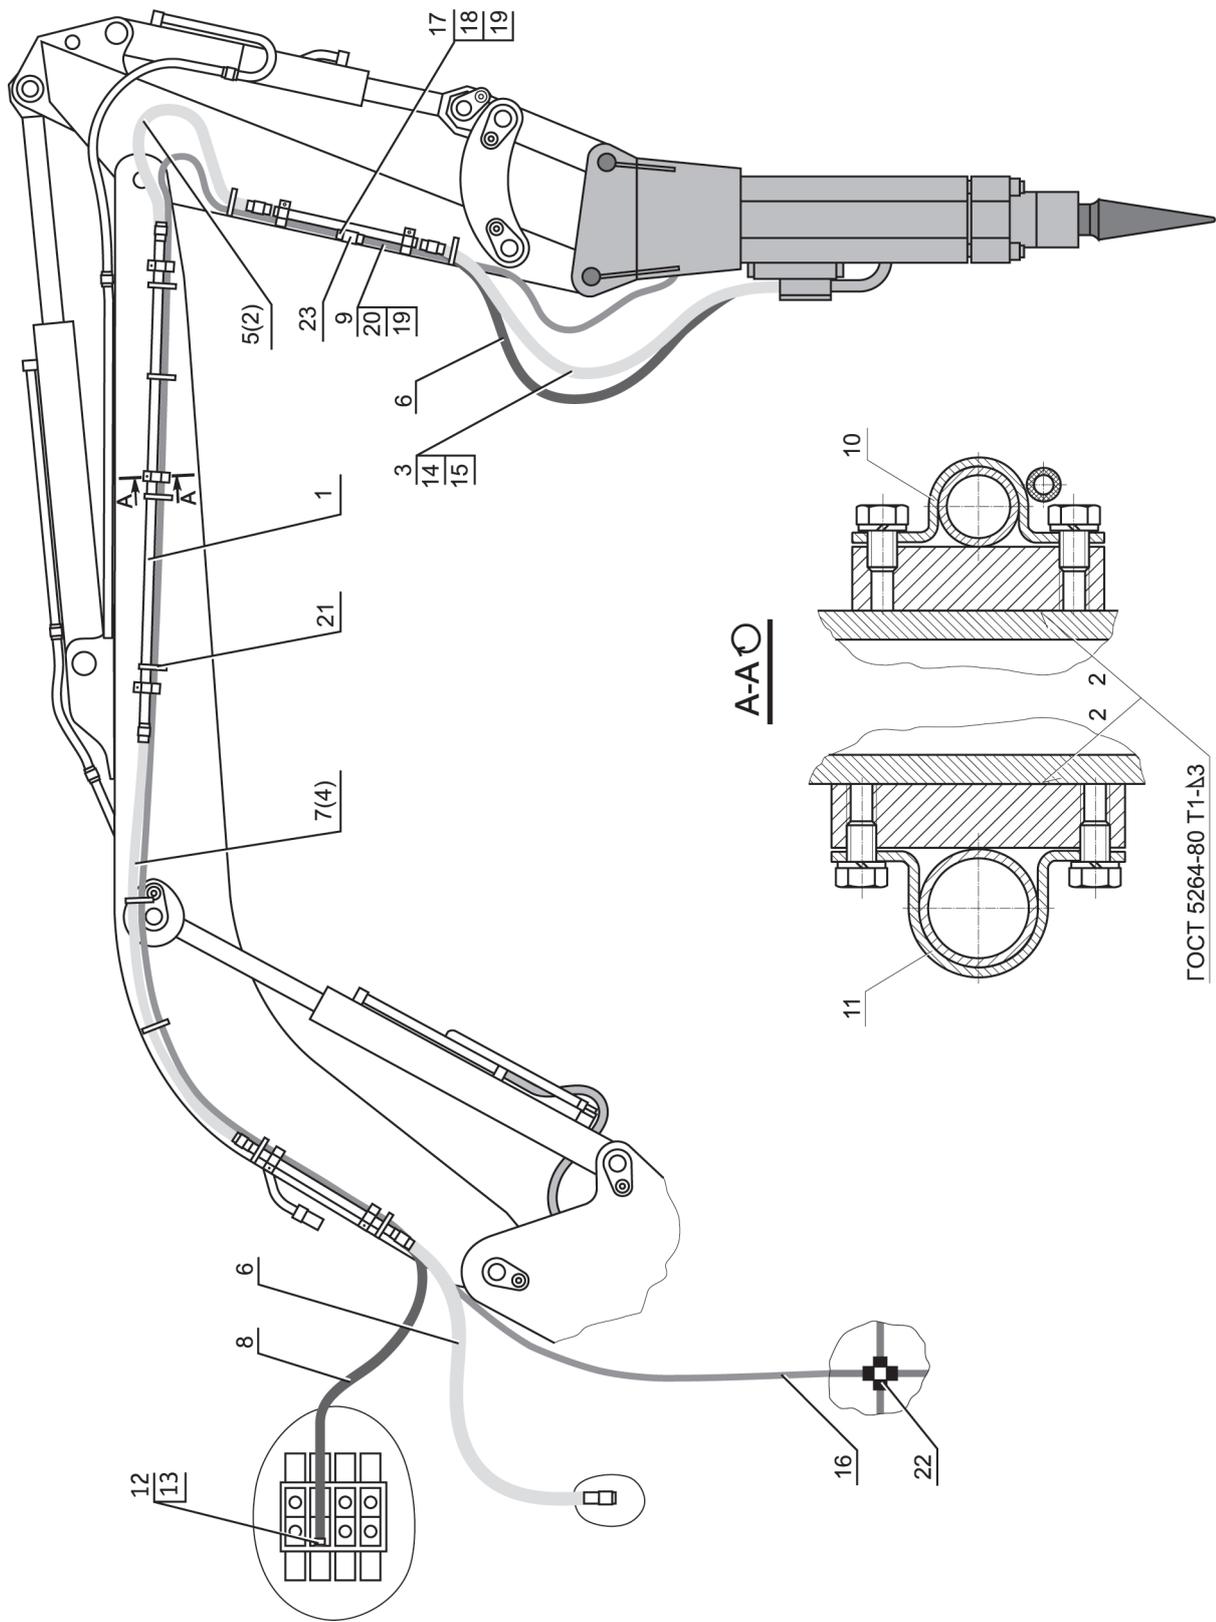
Монтаж гидрооборудования гидромолота на рабочем оборудовании экскаватора ЕК-12
